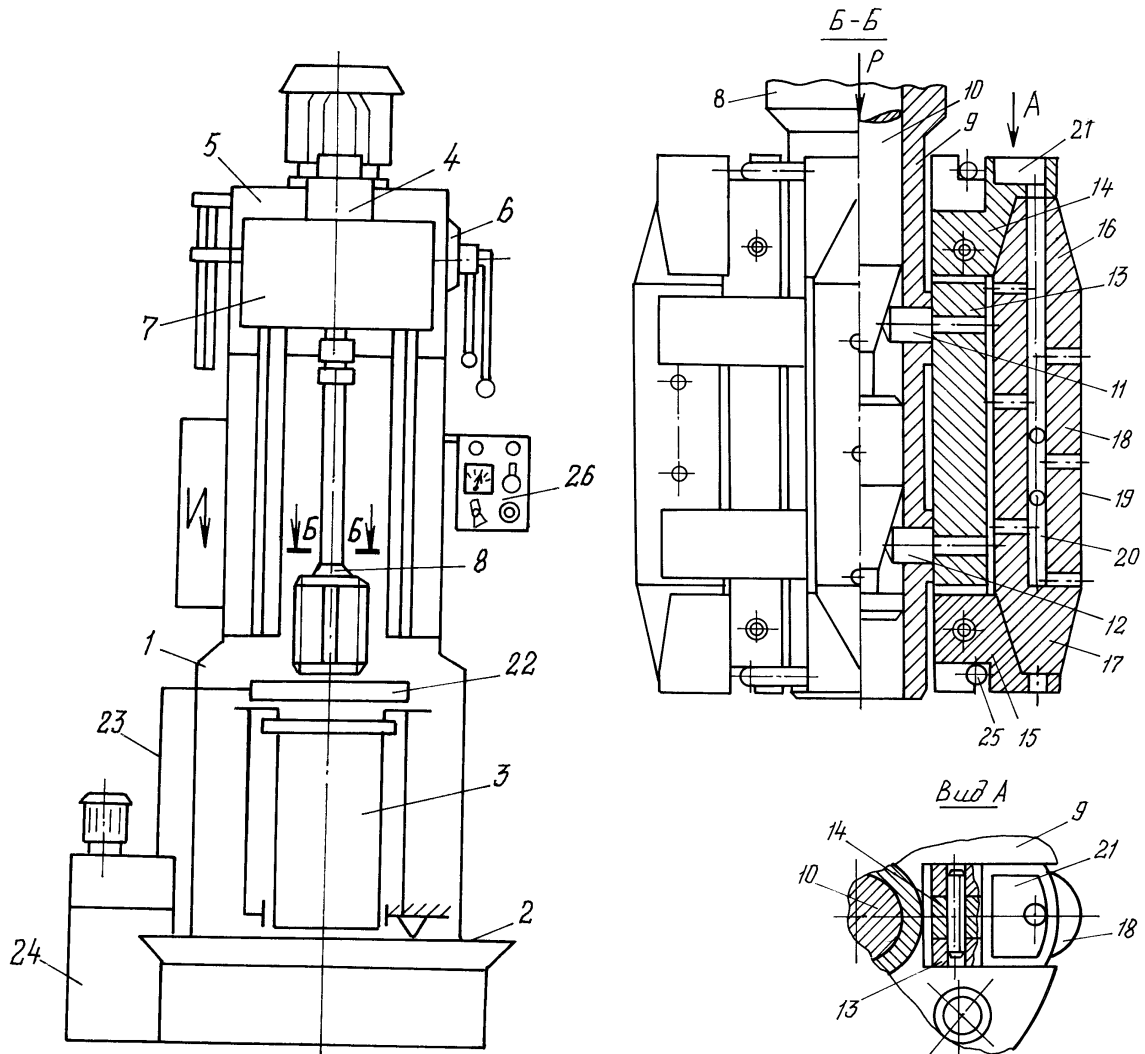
Загальний вигляд пристрою для прецизійного латунювання гільз циліндрів і деталі типу втулка
